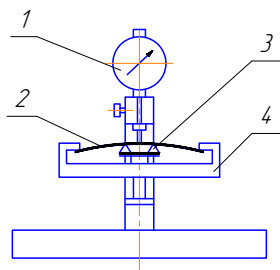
Нагружающее устройство: 1 – головка измерительная часового типа; 2 – образец; 3 – вкладыш; 4 – скоба
